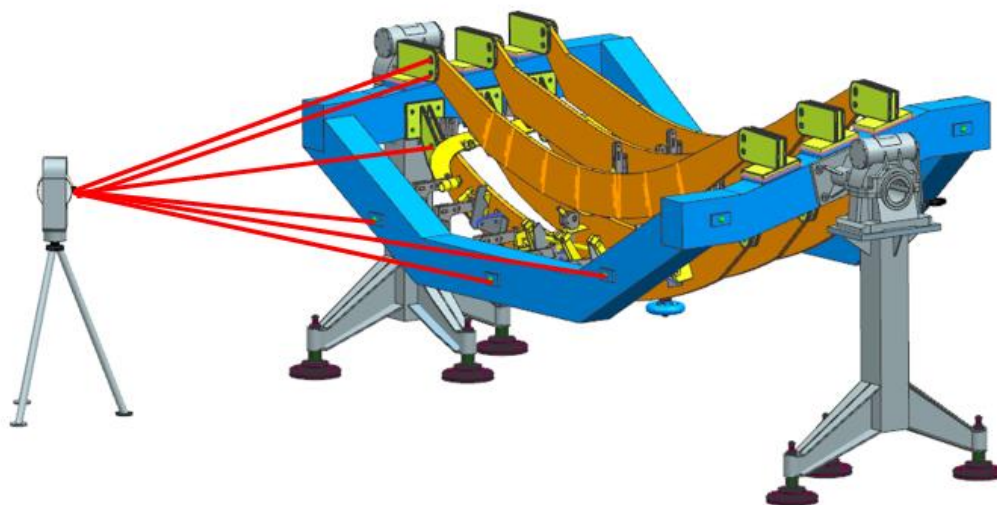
Монтаж сборочного приспособления с помощью трекера
